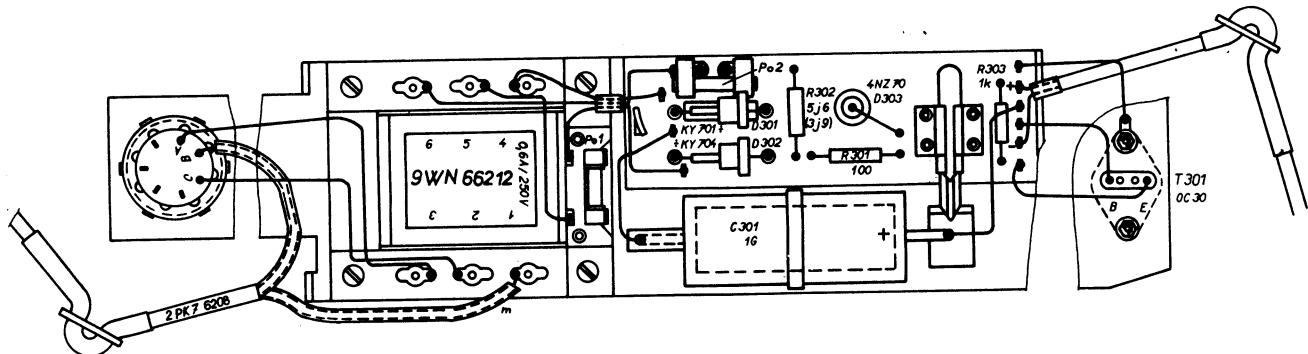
Deska s plošnými spoji pro regulátor motoru A3
